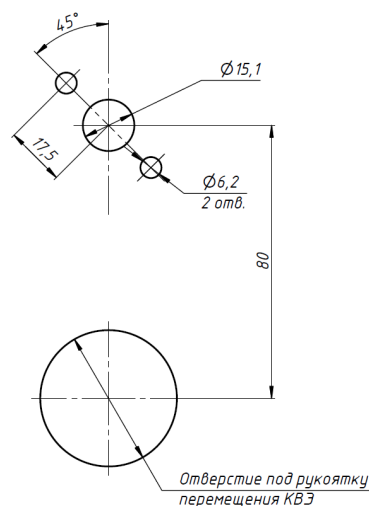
Установочные размеры рукоятки на фасаде КРУ (вид с фасада)
